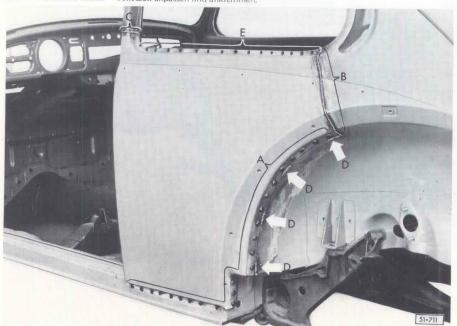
Seitenteil außen – Teilstück einschweißen.
